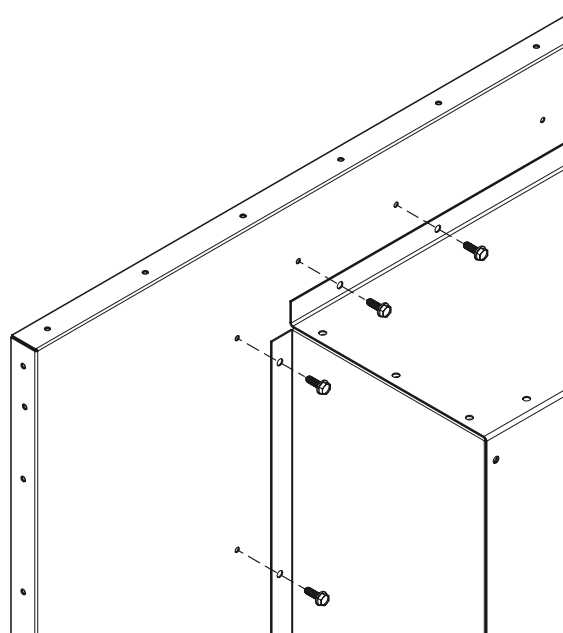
Dettagli di assemblaggio dei silenziatori laterali
